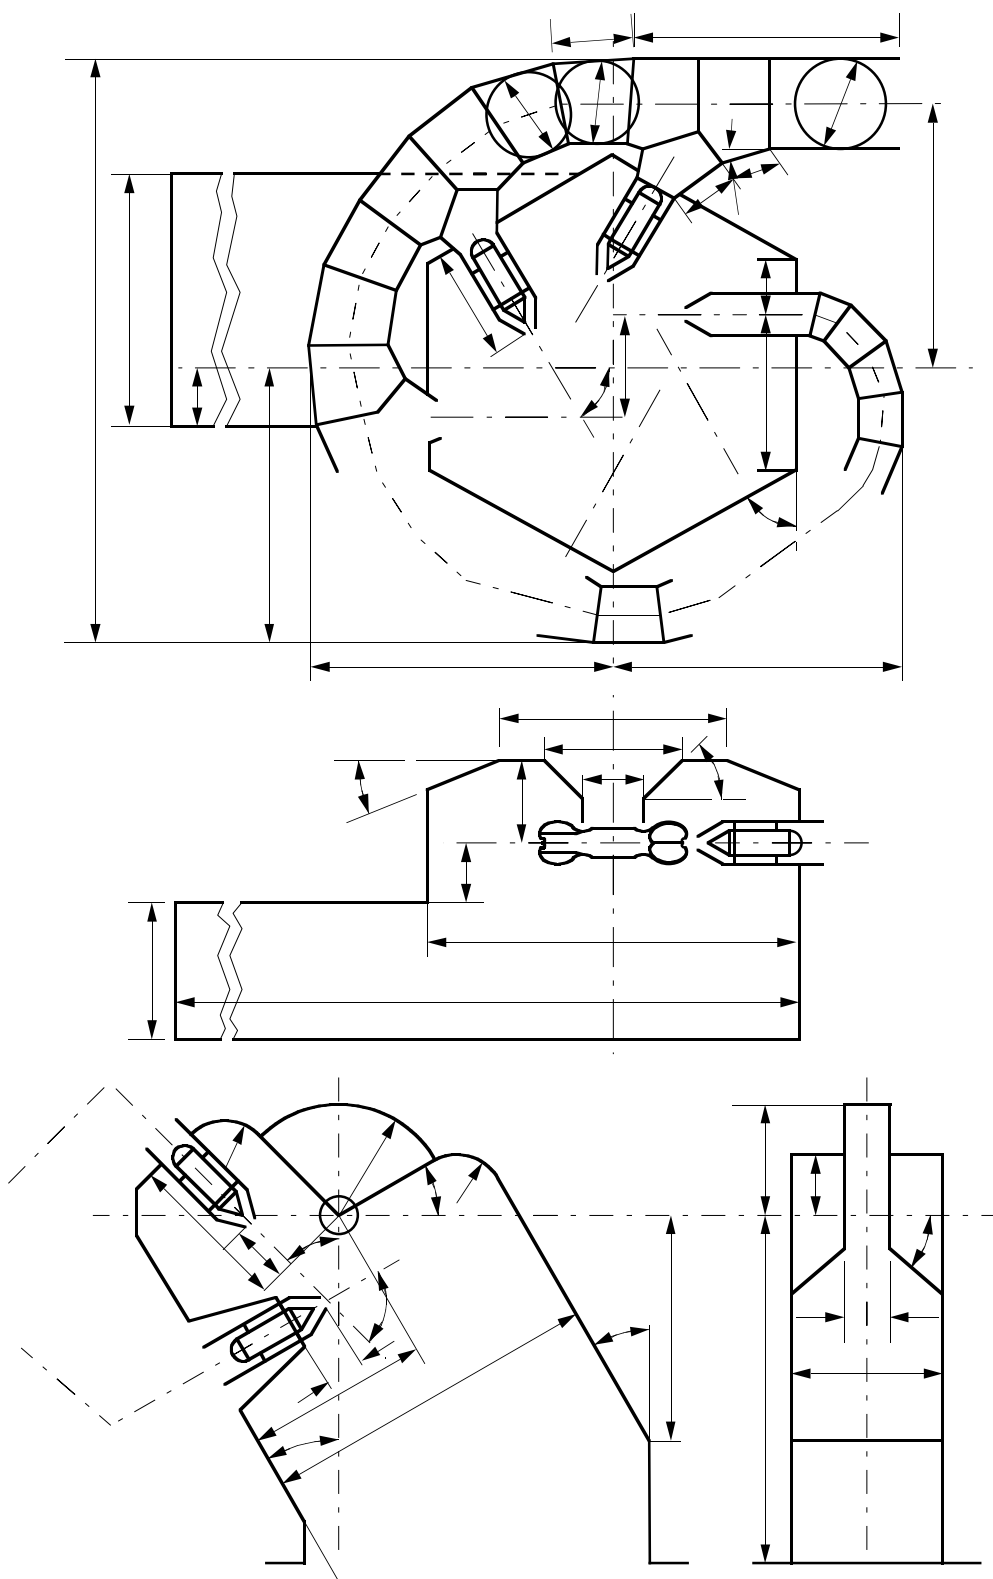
Turbine Pelton: Exemple de dimensions à contrôler sur le distributeur et sur le bâti de machines à axe vertical et horizontal
